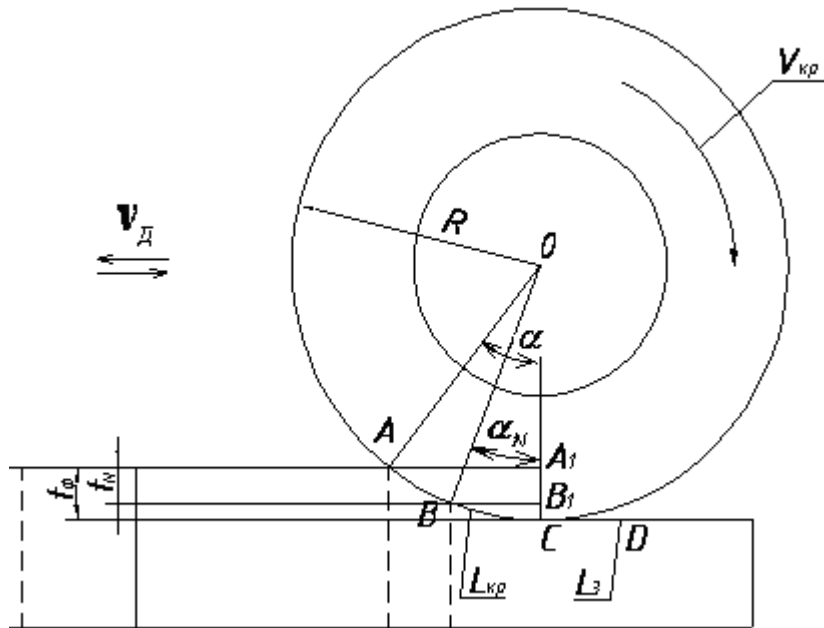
Схема зони контакту шліфувального круга і заготовки
